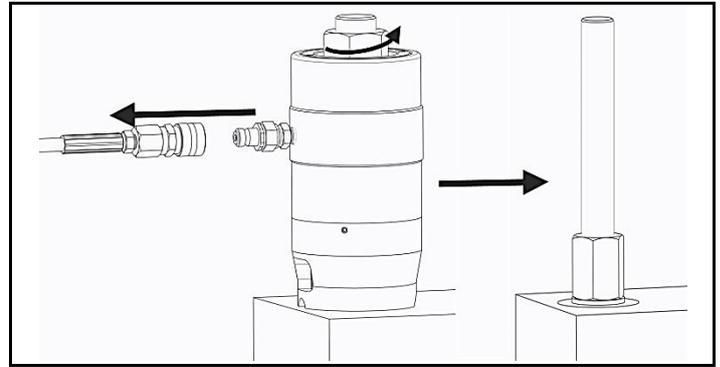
Remova a mangueira, retire e reposicione o tensionador
